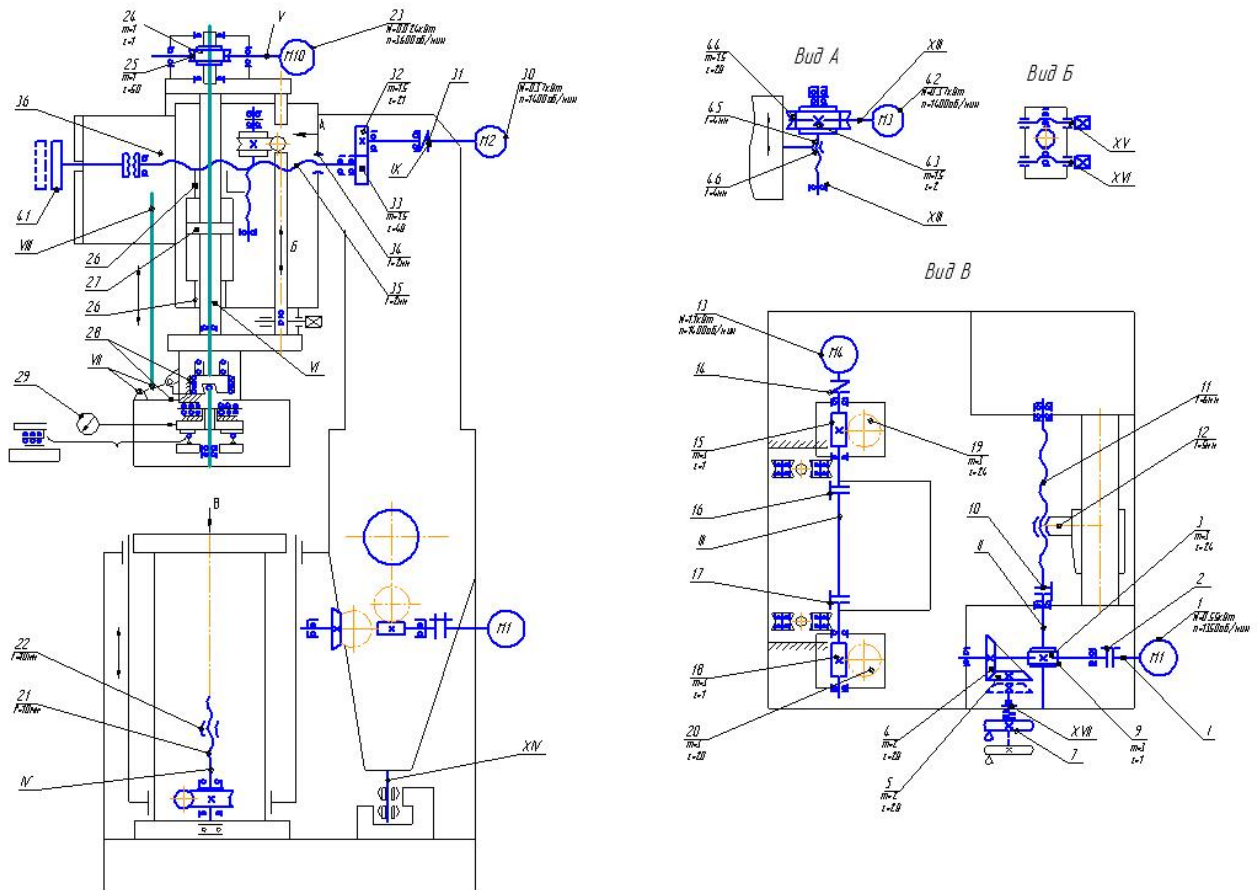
Кинематическая схема станка модели 4E723-01.Ф.
